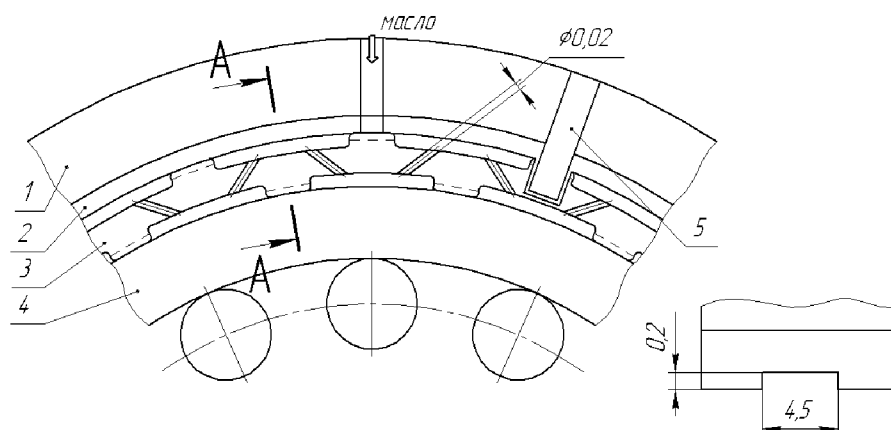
Дроссельный демпфер: 1 – корпус подшипника; 2 – втулка стальная; 3 – втулка Аллисона; 4 – наружное кольцо подшипника; 5 – штифт, фиксирующий вибратор от поворота
